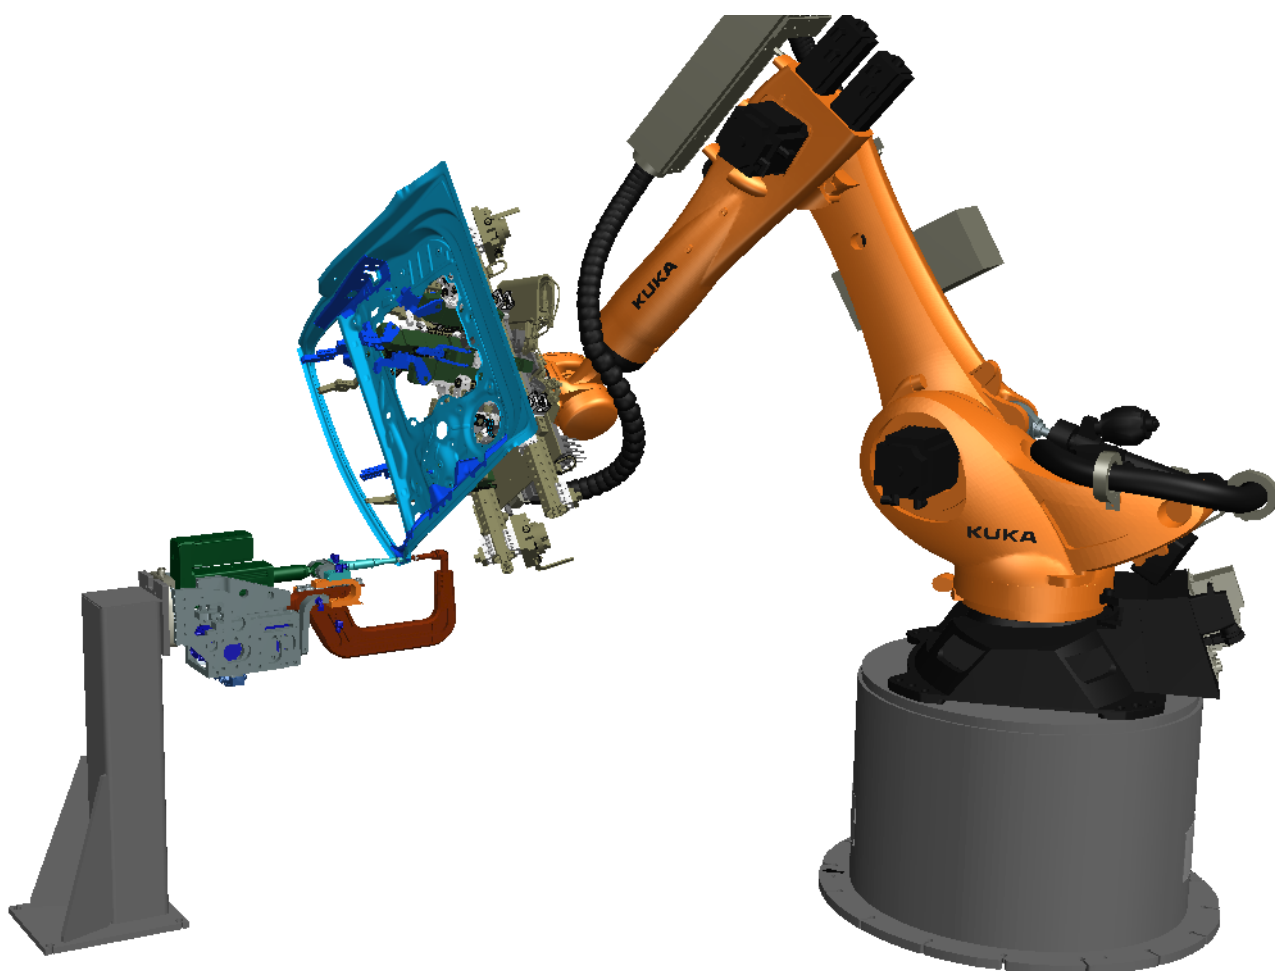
Положение робота и автодетали в процессе сварки
